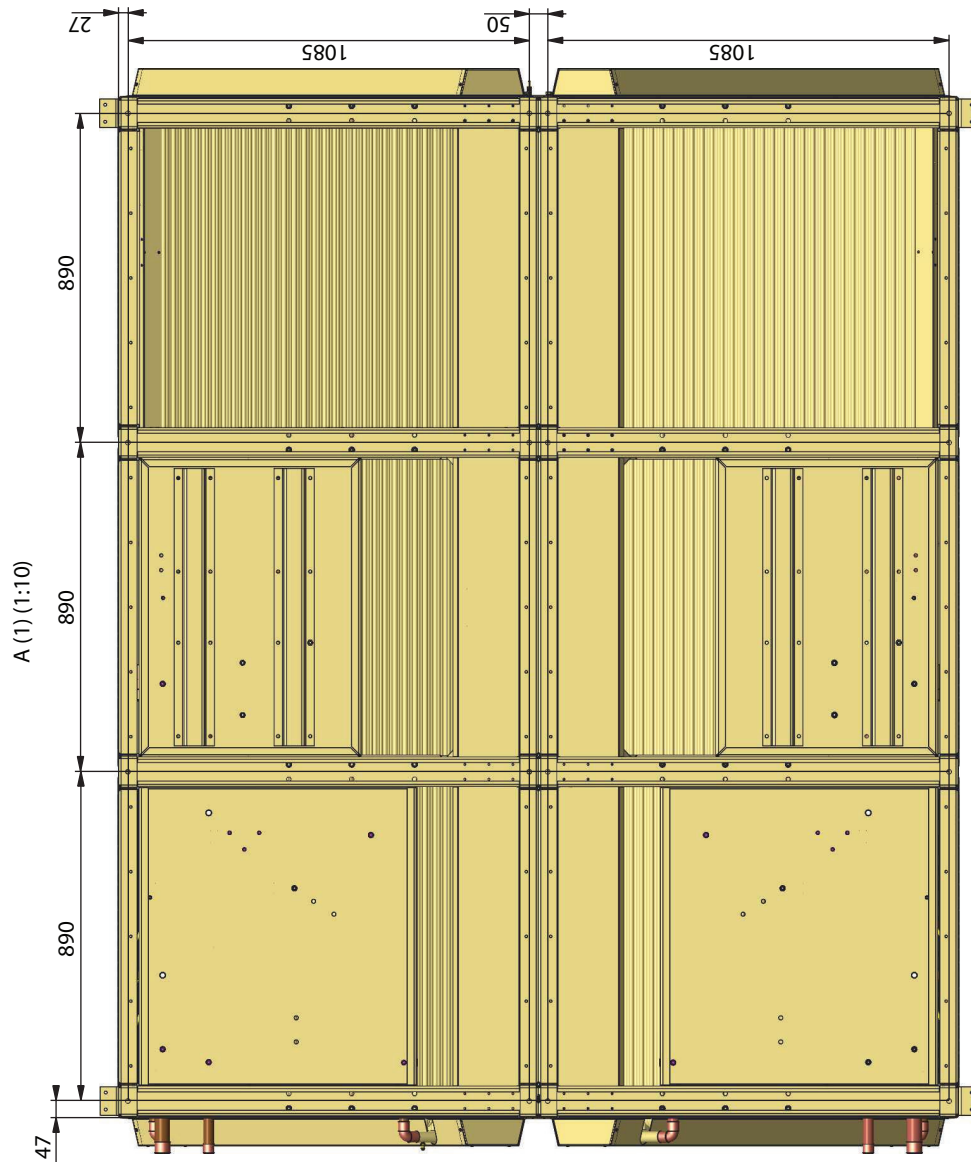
Агрегат компрессорный МАКК 120-1902
